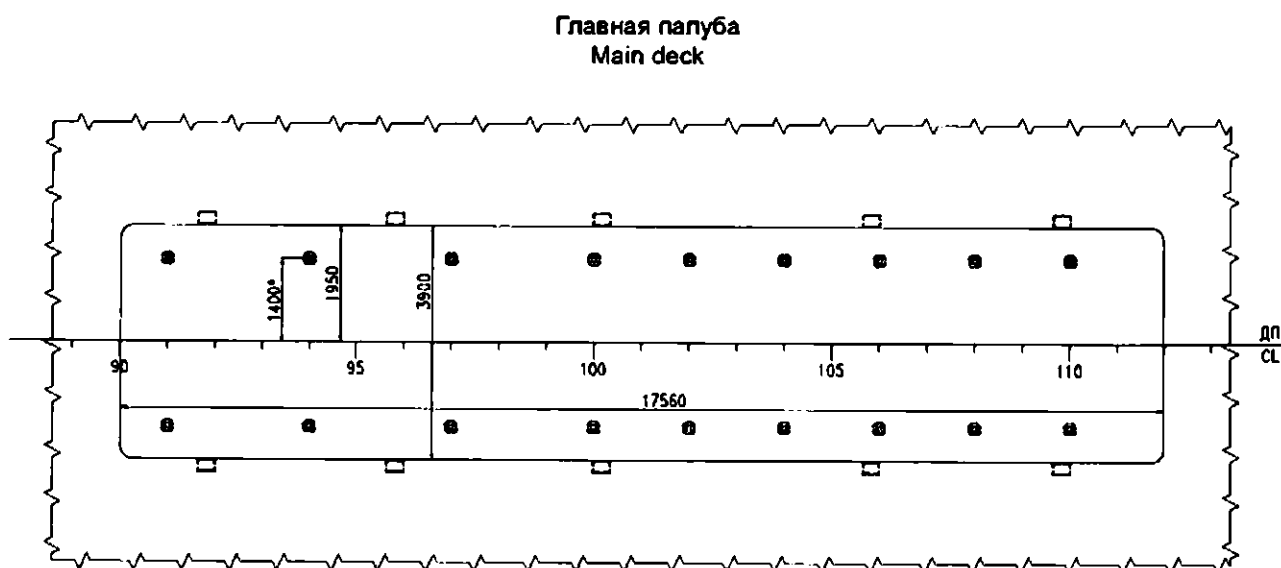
Габаритные размеры вид сверху / Overall dimensions top view.
